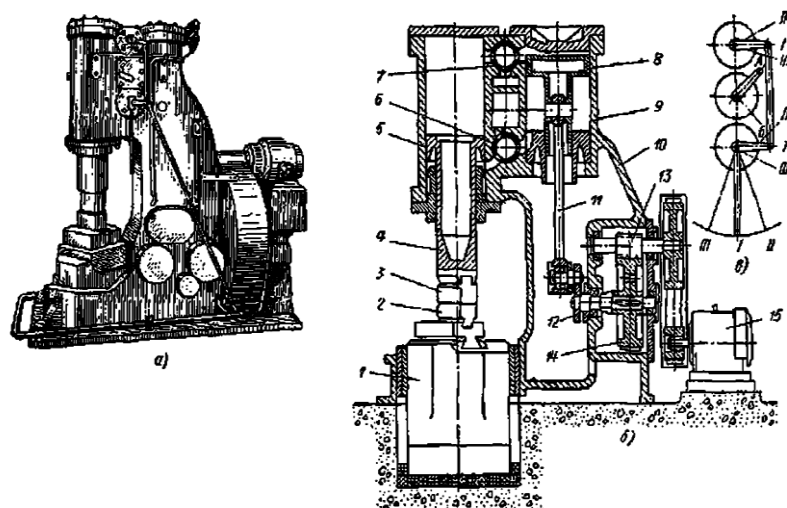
а - общий вид и б - схема пневматического молота :1 – шабот; 2 – нижний боек; 3 – верхний боек; 4 – рабочий поршень; 5 – рабочий цилиндр; 6 – нижний кран; 7 – верхний кран; 8 – компрессорный поршень; 9 – компрессорный цилиндр; 10 – станина; 11 – шатун; 12 – кривошип; 13 – зубчатая шестерня; 14 – зубчатая шестерня; 15 – электродвигатель
